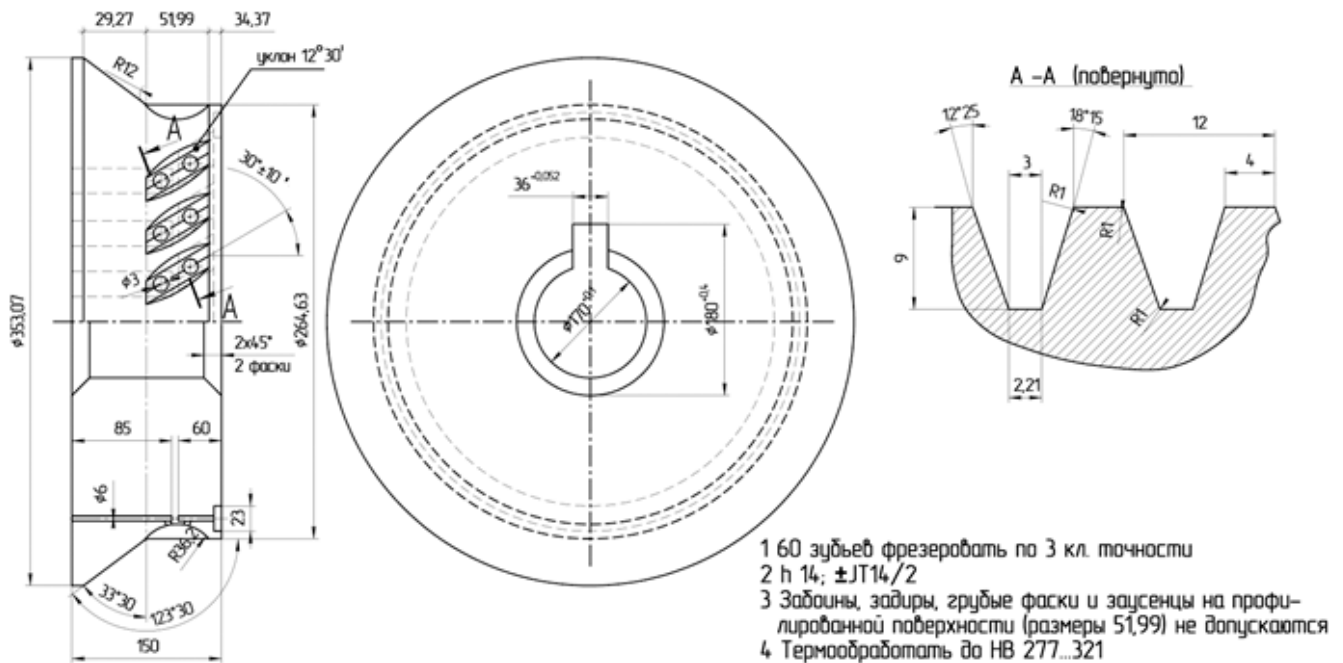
Зубчатый бандаж с осевыми каналами для опробования нового способа прокатки
